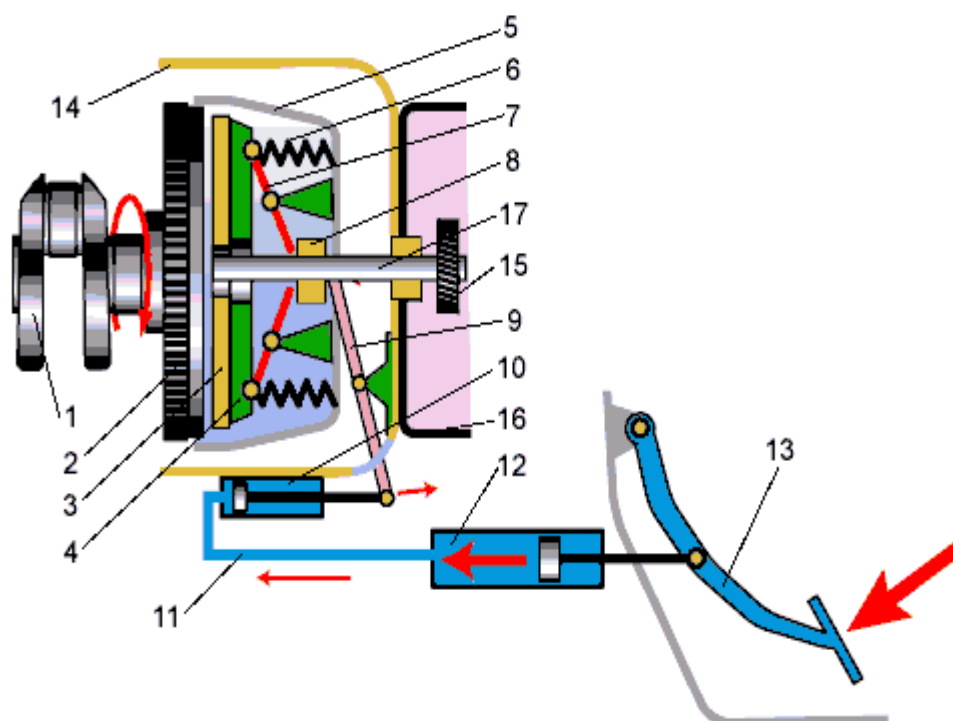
Схема гидравлического привода выключения сцепления и механизма сцепления
